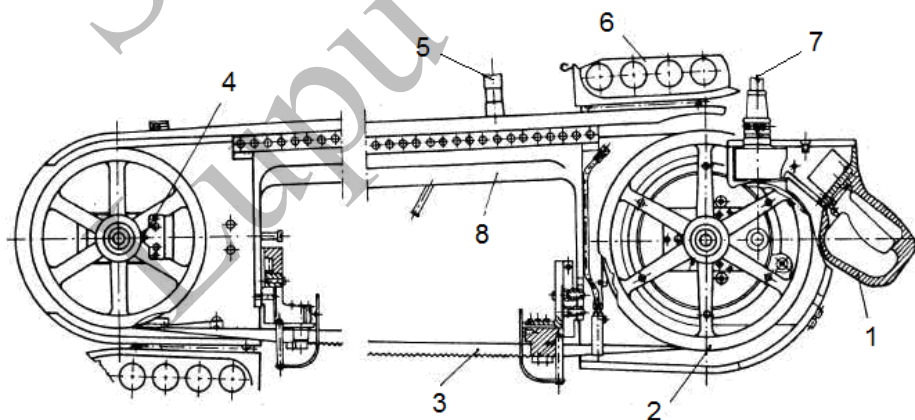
Fierăstrău mobil cu pânză cu mișcare continuă: 1- mâner cu contactor; 2- roată antrenare; 3- pânză fierăstrău; 4- roată întindere; 5- prindere la scripete cu contragreutăți; 6- role ghidare; 7- sistem de prindere la scripete cu cablu electric de alimentare
